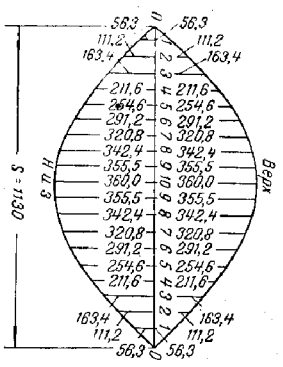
Разметка отверстия в стволе сварного тройника.
